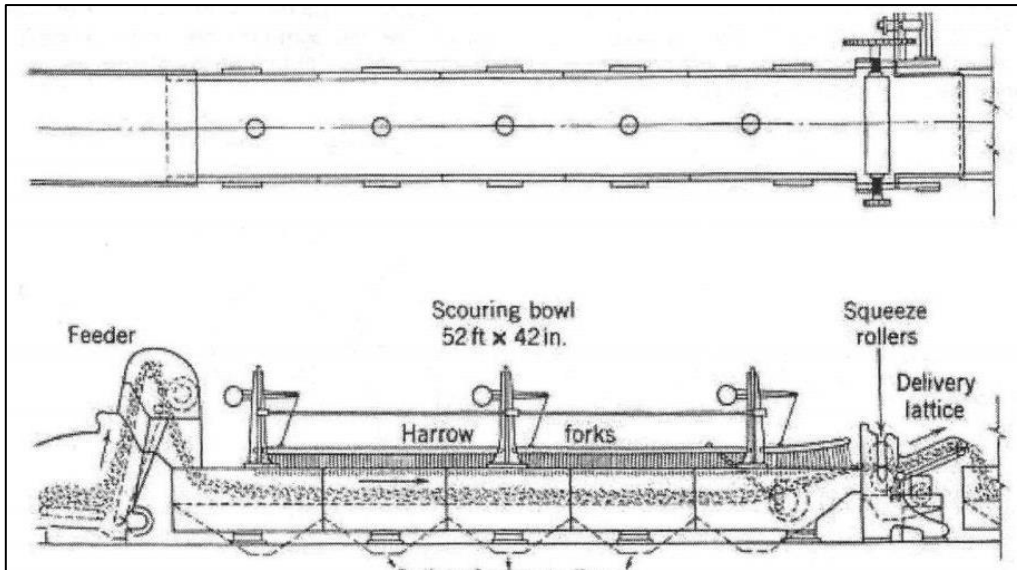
Baño de lavado con sistema de transporte a rastrillera
